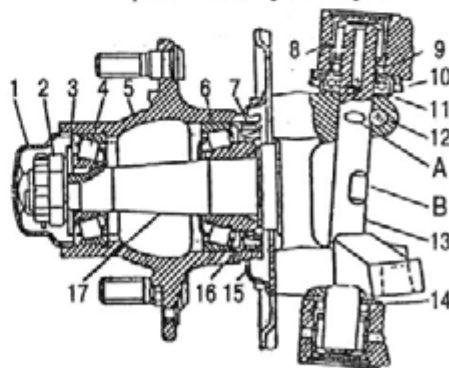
Поворотный кулак и ступица переднего колеса: 1 - колпак ступицы; 2 - гайка; 3 - стопорная шайба; 4 - наружный роликовый подшипник; 5 - ступица; 6 - внутренний роликовый подшипник; 7 - манжета; 8 - игольчатый подшипник; 9 - резиновое уплотнительное кольцо; 10 - уплотнитель упорного подшипника; 11 - упорный шариковый подшипник; 12 - стопорный штифт; 13 - шкворень; 14 - регулировочная шайба; 15 - маслоотражатель; 16 - упорная шайба; 17 - поворотный кулак; А - лыска под штифт; В - лыска под ключ
